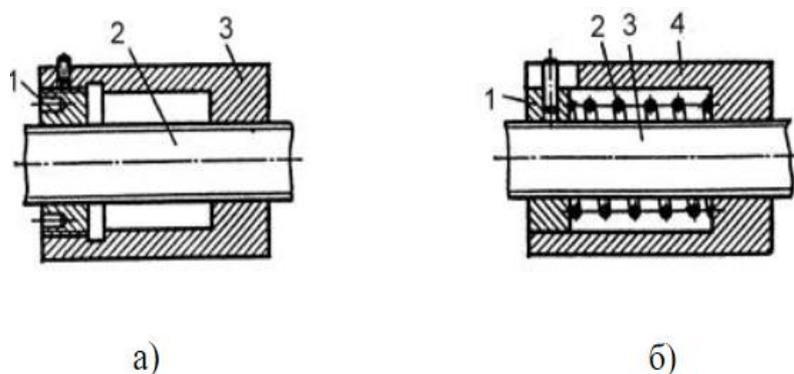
Конструкция люфтовывбирающего механизма с разрезной гайкой
